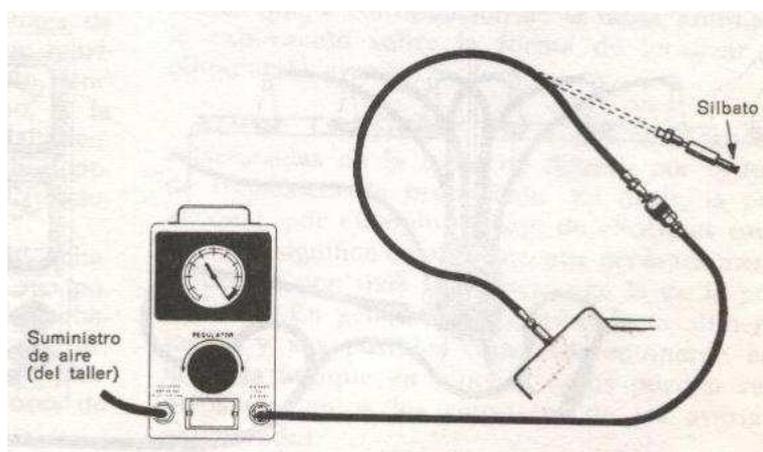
Empleo de un comprobador de fugas para cilindros.
